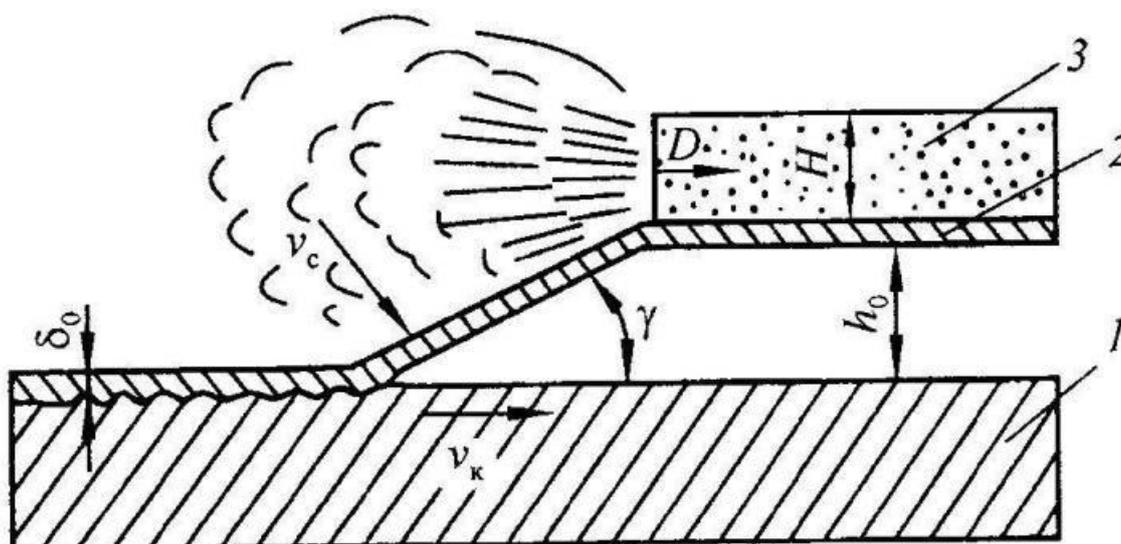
Схема сварки листов металла сваркой взрывом: 1 – основной слой плакированной стали; 2 – плакирующий слой; 3 – взрывчатое вещество; h_0 – зазор, необходимый для придания метаемой пластины необходимой скорости; D – детонатор; V_k – скорость метаемой пластины
